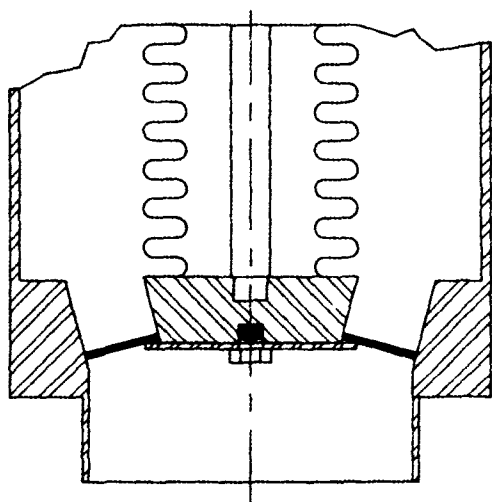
Схема уплотнения твердый — твердый металл, используемой компанией VAT VACUUM-VENTILE AG в клапанах с металлическим уплотнением. Коническое седло, наконечник и коническая шайба изготовлены из твердых нержавеющей сталей. Обратите внимание, что шайба должна быть герметичной как на своем внутреннем, так и на внешнем диаметре
